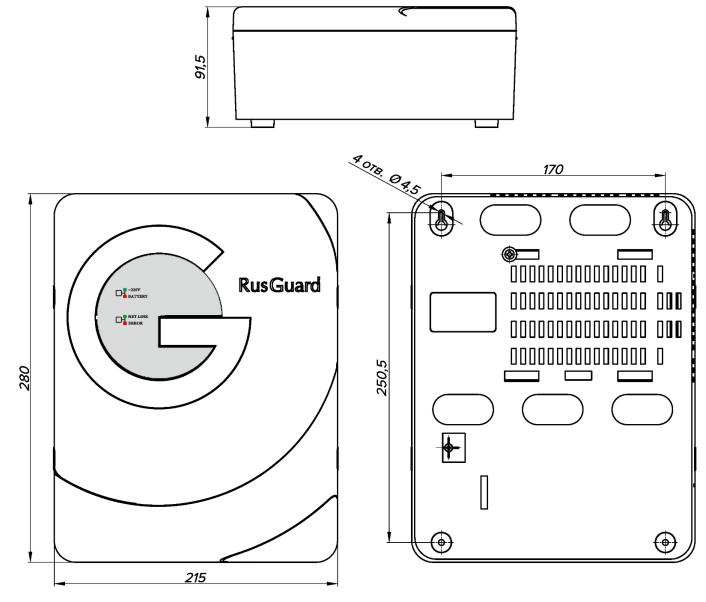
Габаритные размеры и крепеж контроллера в корпусе исполнения -В
